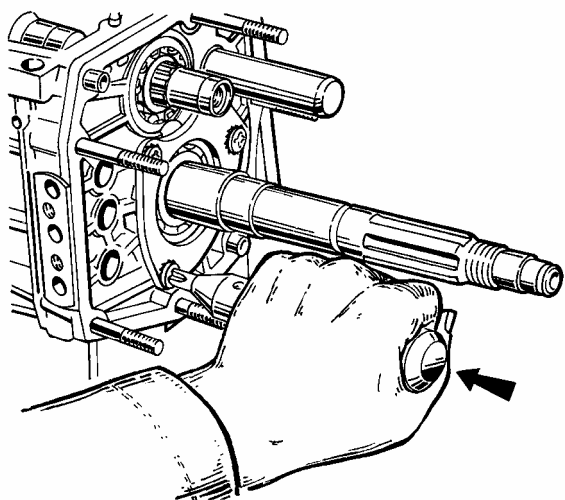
Отвертывание винтов крепления стопорной пластины промежуточного подшипника вторичного вала дрель-отверткой.
